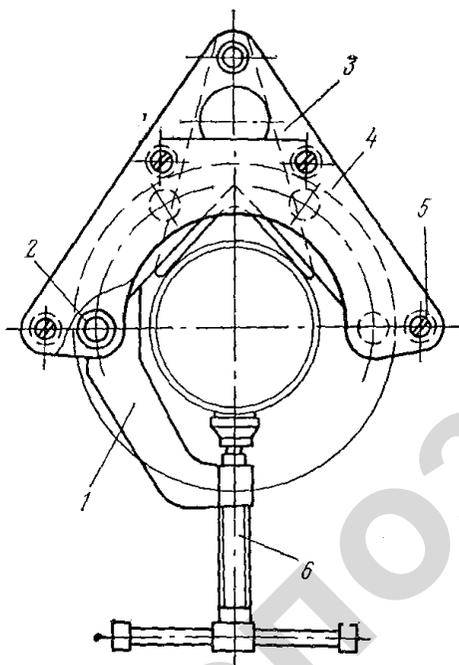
Схема приспособления для приварки фланцев к трубам:
